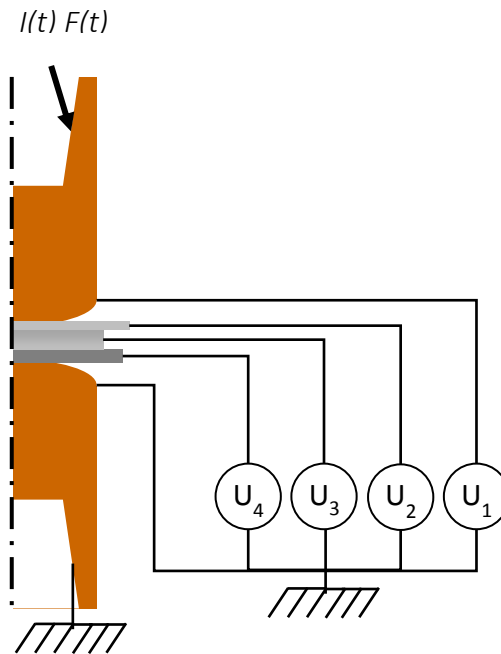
Implantation des mesures de tensions pour chaque tôle.
